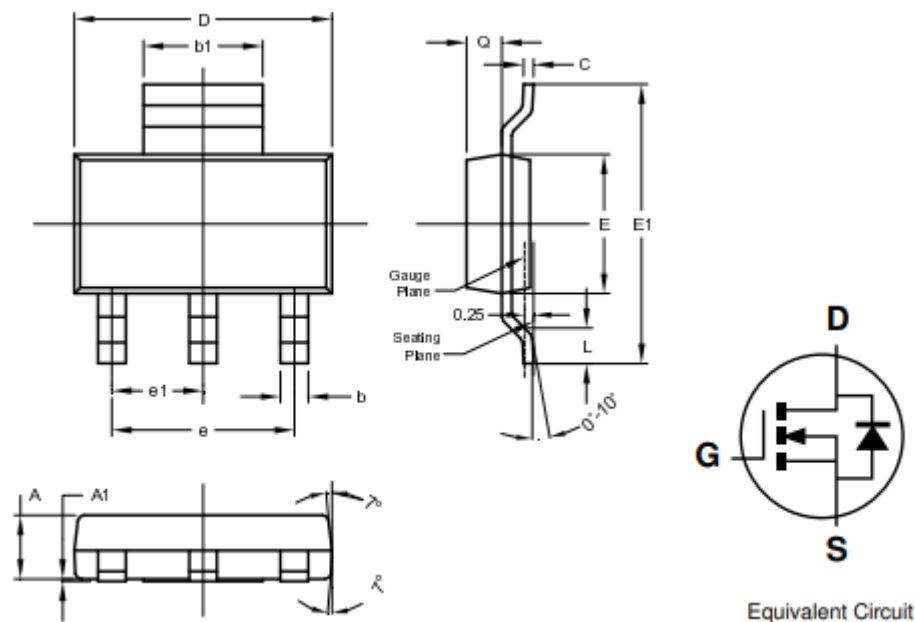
Габаритный чертеж полевого транзистора типа ZVN4206GTA
